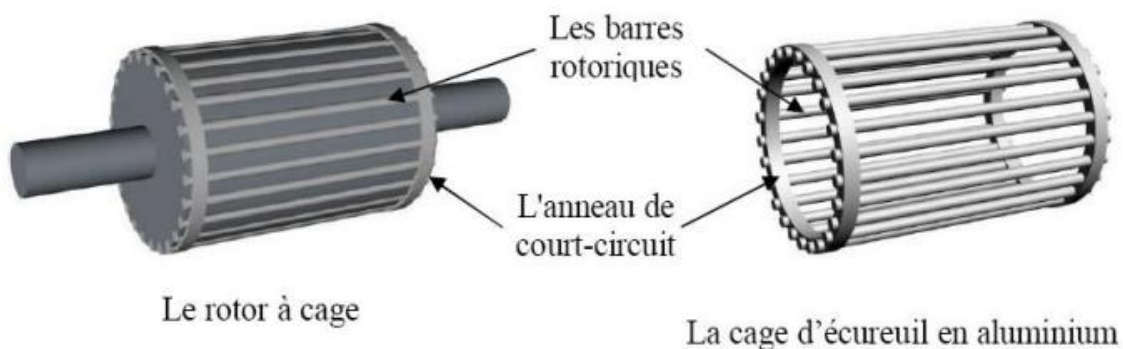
Rotor de la machine asynchrone triphasée à cage.
